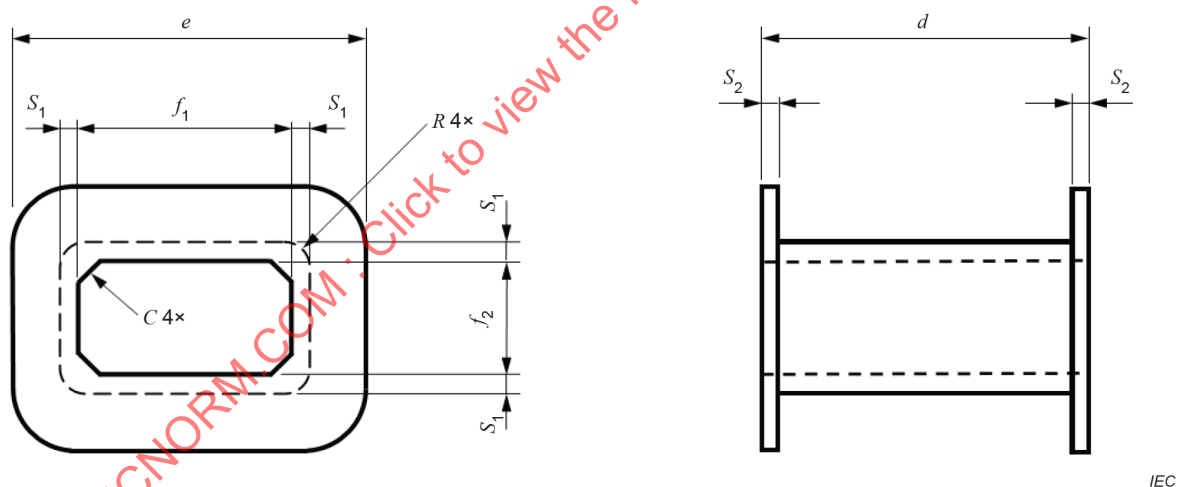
Dimensions principales des supports de bobine pour les noyaux EFD
